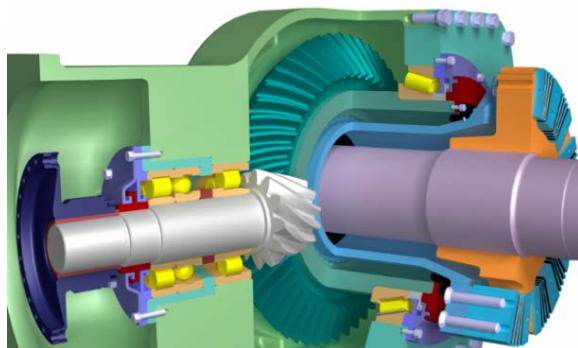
3D-модель редуктора колесной пары в разрезе
